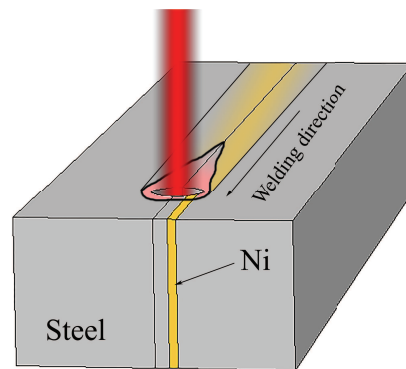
Configuration de soudage décalée de 200 μm (soudure 2)
